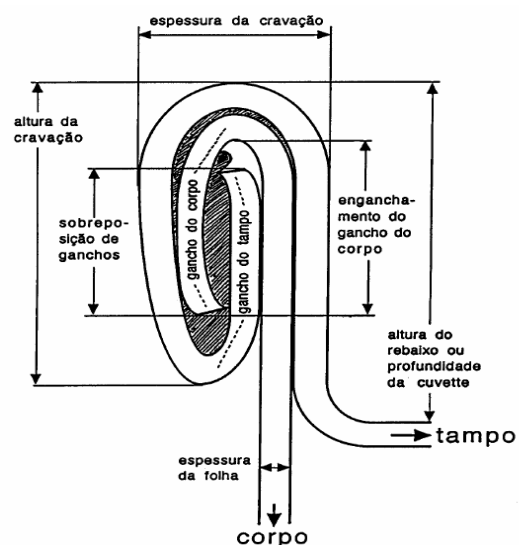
Plano de cravação (Vaz-Pires, 2006).
